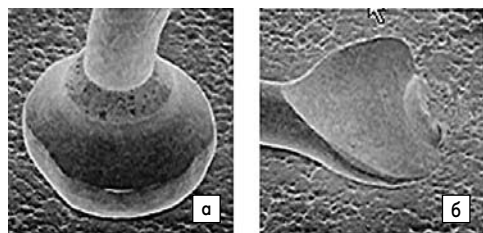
Внешний вид соединения, полученных методом «шарик-клин»: а) первой сварки; б) второй сварки
